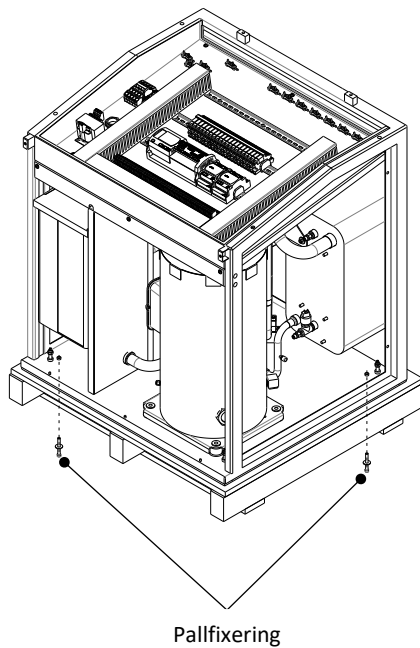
Demontering av skruvarna som fixerar värmepumpen mot pallen.
